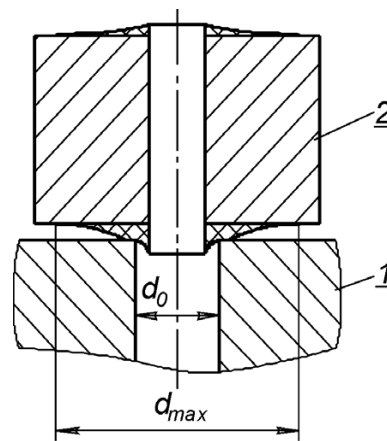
Схема напылов металла на торцах заготовок, обработанных дорнованием:
